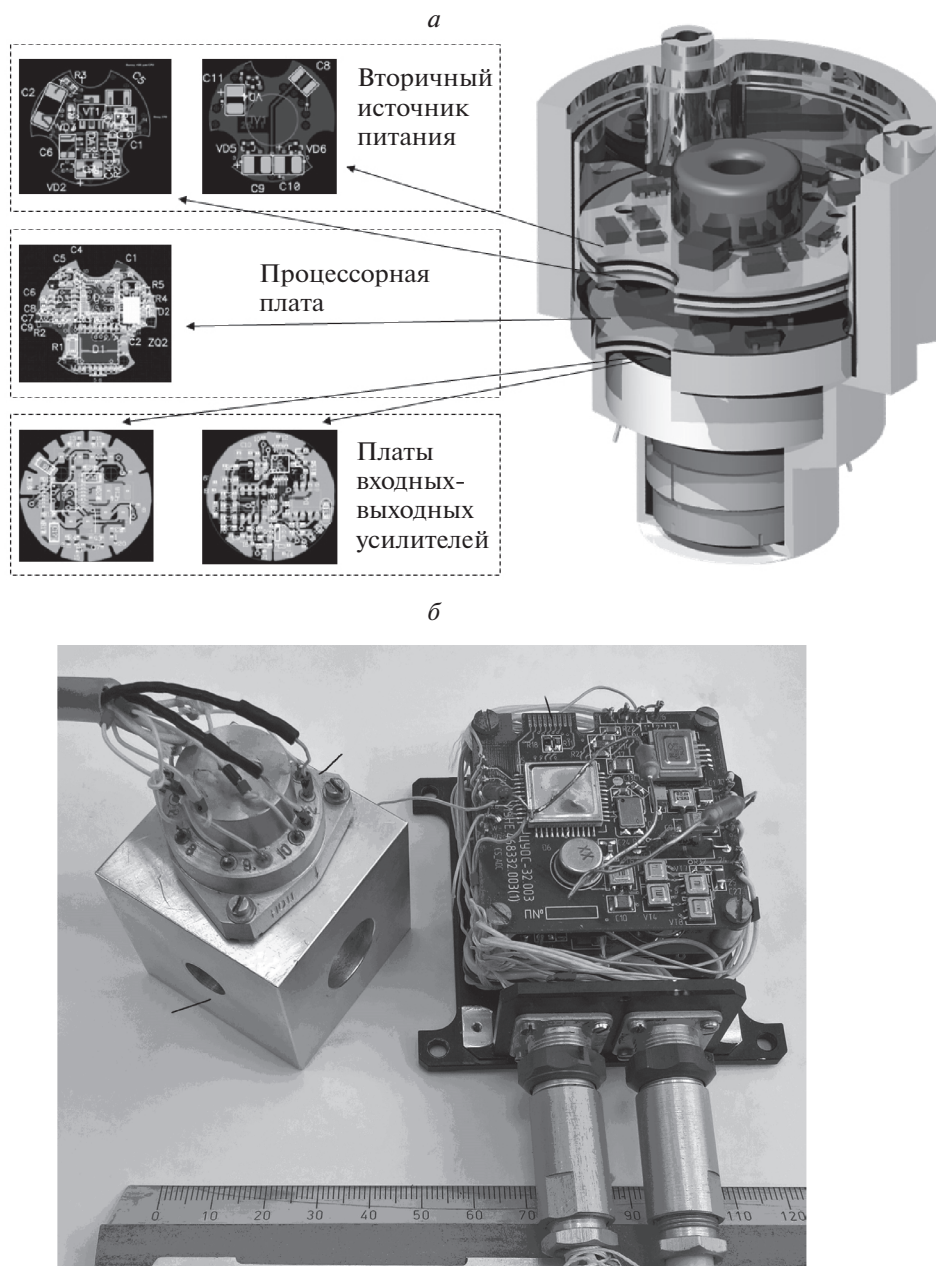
Внешний вид КМА с ЦУОС: а – 3D-модель, б – фото макетного образца
